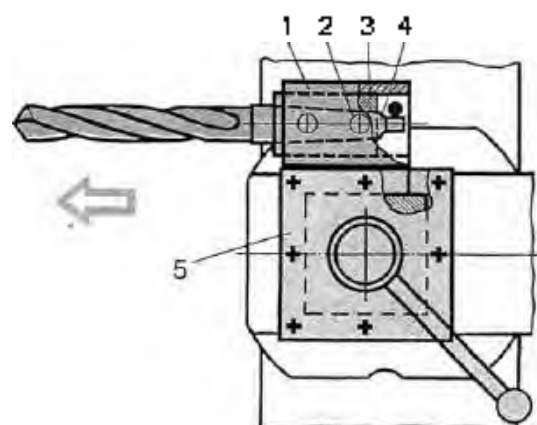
ДЕРЖАВКА ДЛЯ СТЕРЖНЕВИХ ІНСТРУМЕНТІВ (ВЕРСТАТ 16К20)
